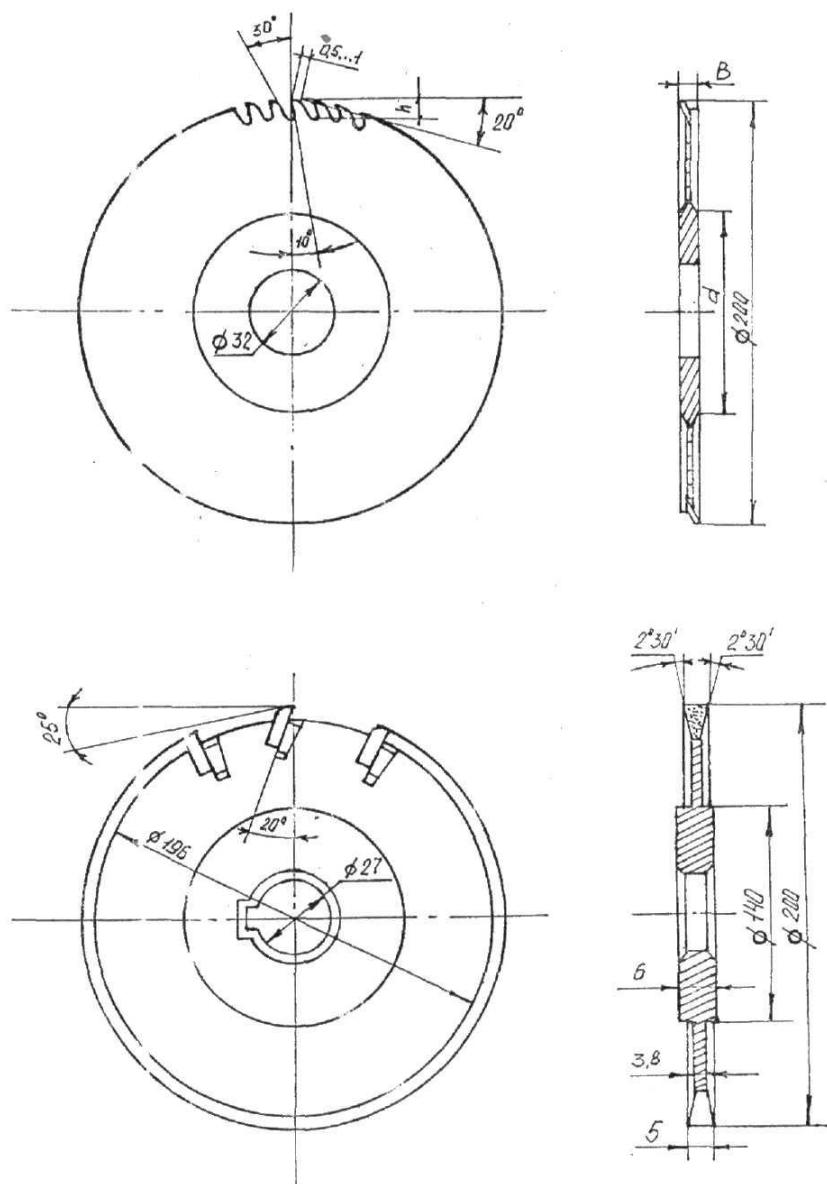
Высокопроизводительная отрезная фреза и фреза с механическим креплением пластинок из твердого сплава ВКБ
